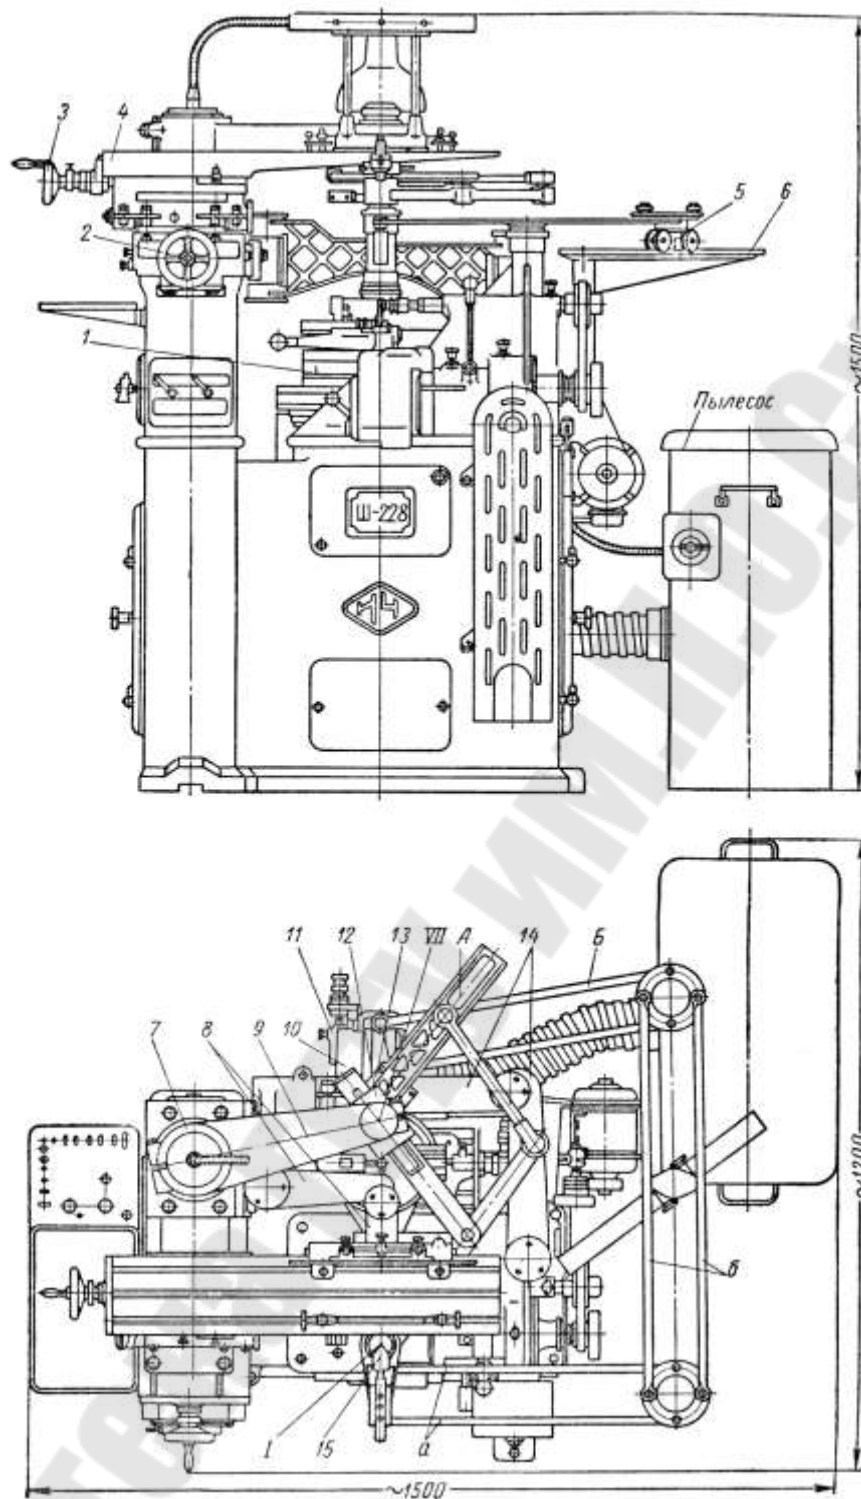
Общий вид профилешлифовального станка модели Ш-228
